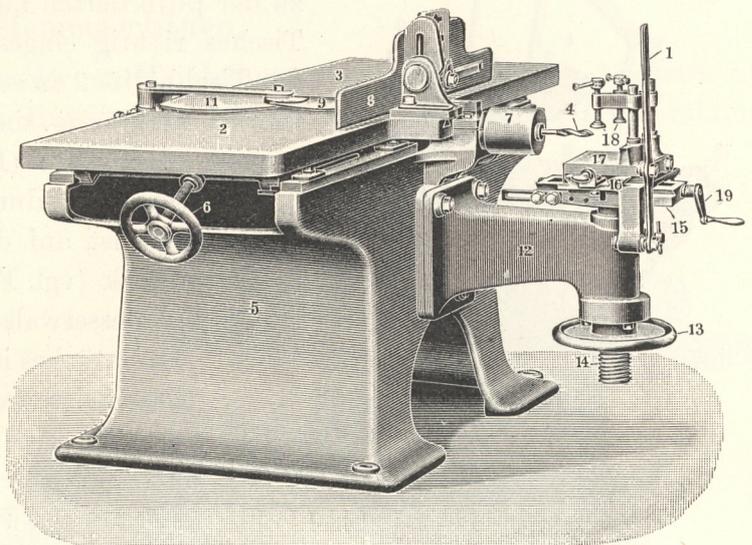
Abrichtmaschine mit Bohrvorrichtung.
